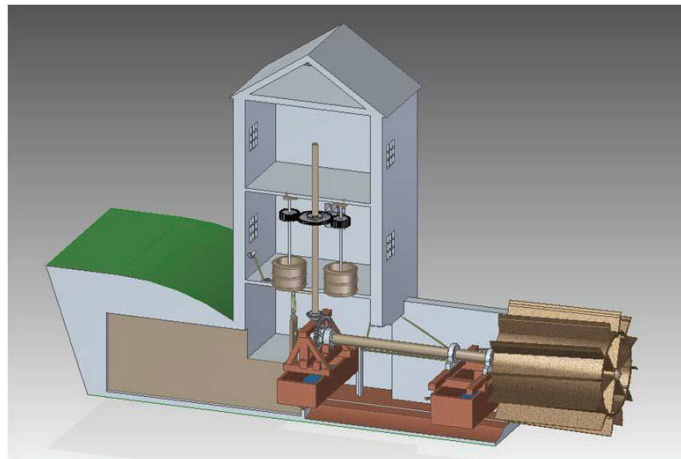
Perspectiva axonométrica dimétrica del conjunto ensamblado.
